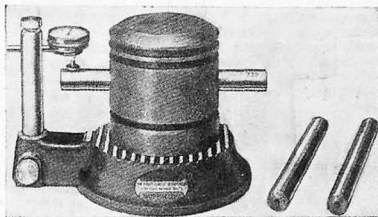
Индикатор с приспособлением для проверки правильности развертки отверстий в поршне для пальца
